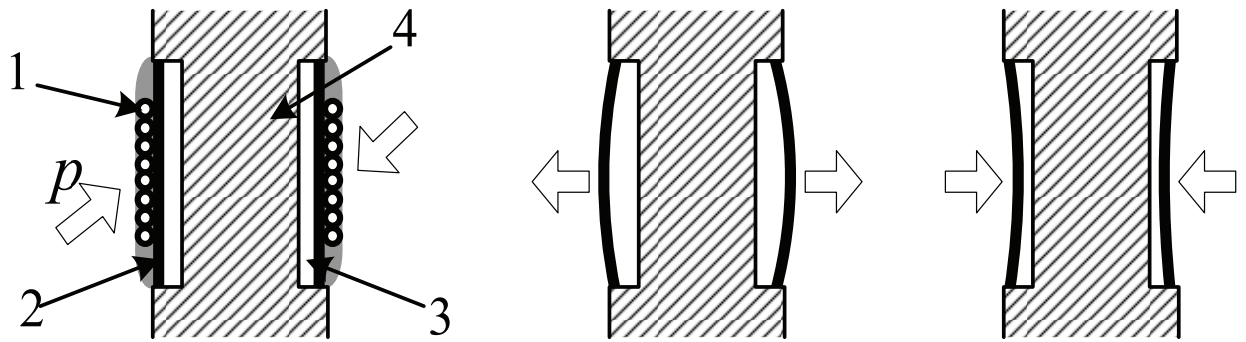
Преобразователь на основе металлического цилиндра
